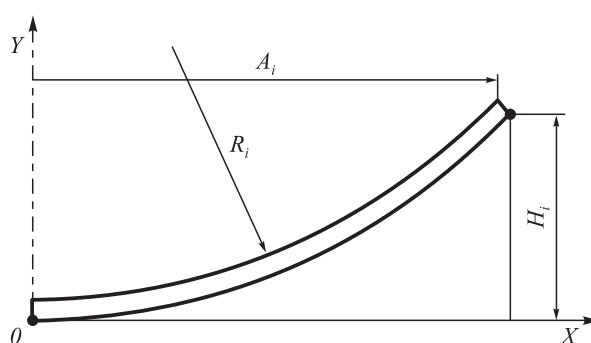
Параметры поперечного сечения заготовки в очаге сворачивания первой формовочной клетки:
